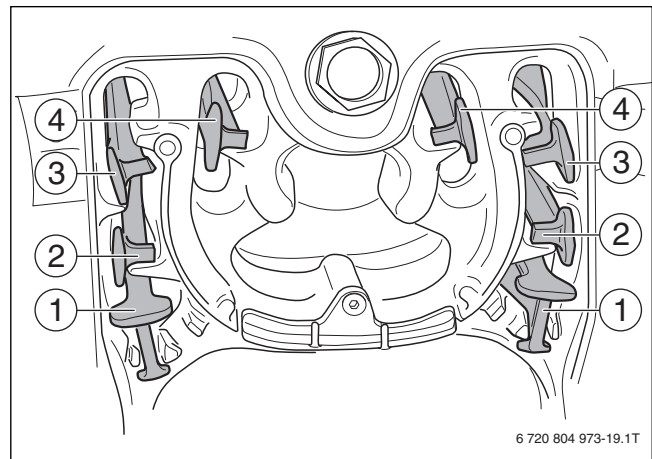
Placas conductoras del gas caliente 18, 22, 30 kW
